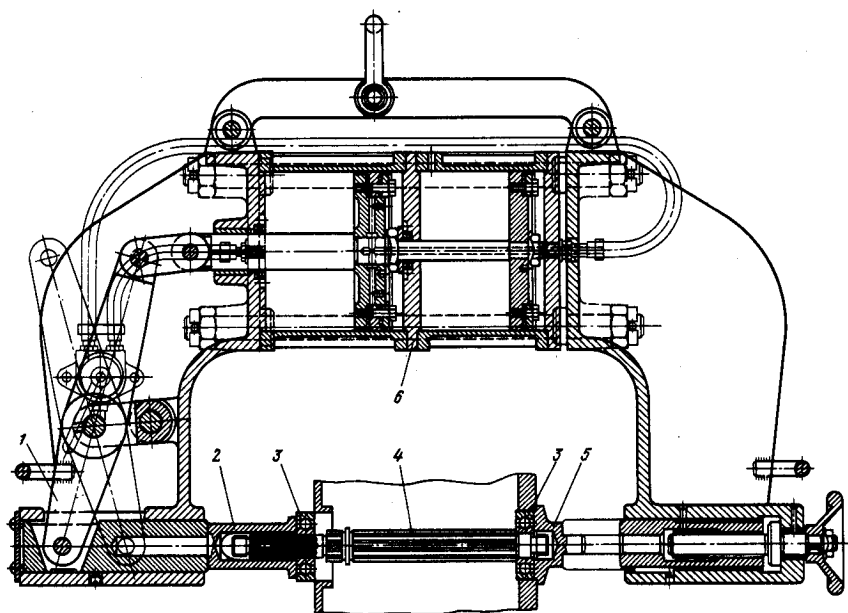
Установка подшипников при сборке коробок передач с помощью подвесной скобы
